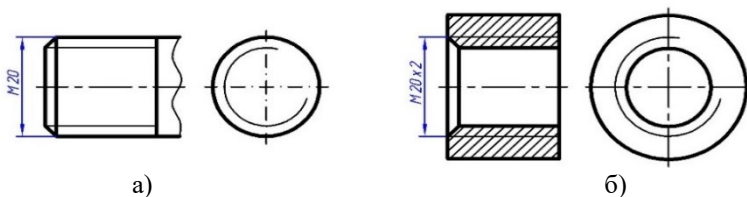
Позначення циліндричної нарізі на кресленнику, крім трубної циліндричної
